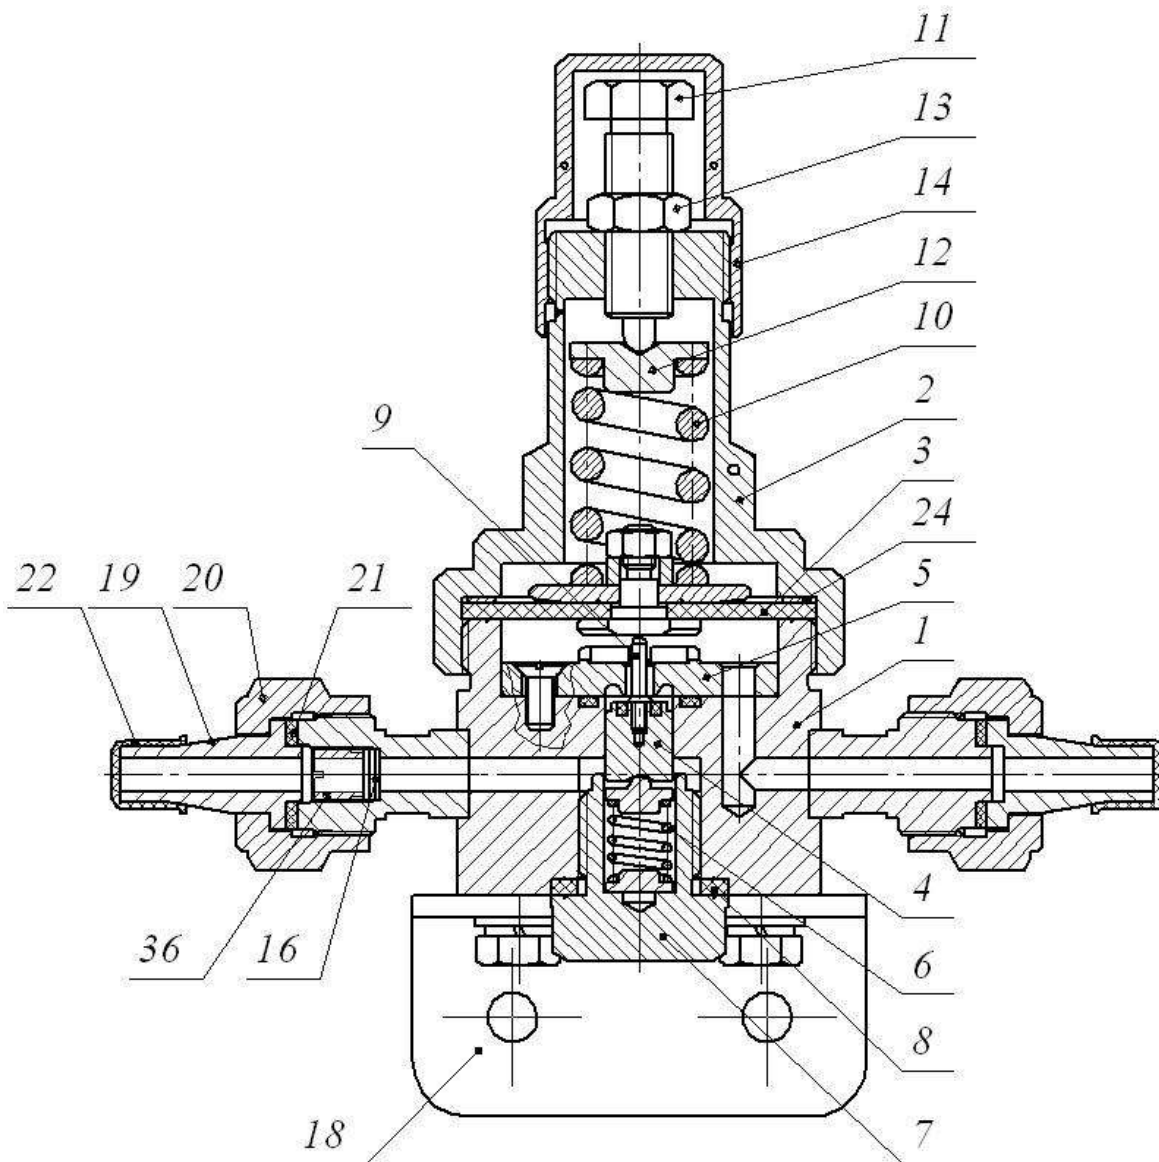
Конструкция редуктора РДФ-7-10-П
